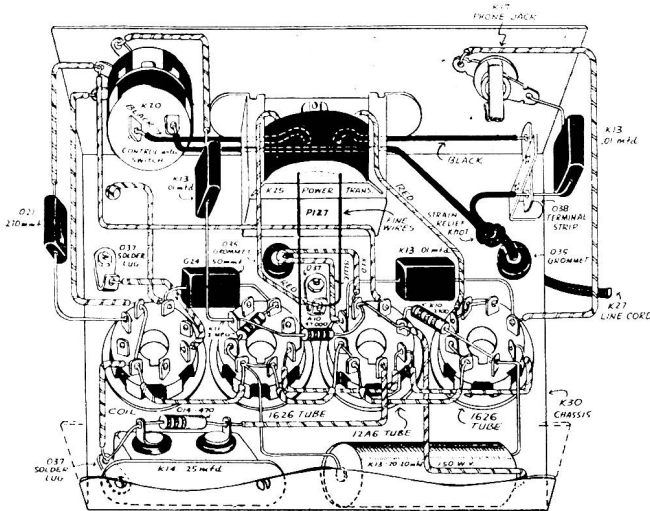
Unteransicht des montierten und verdrahteten Chassis. (Die eingezeichneten Nummern beziehen sich auf die Stückliste.)
